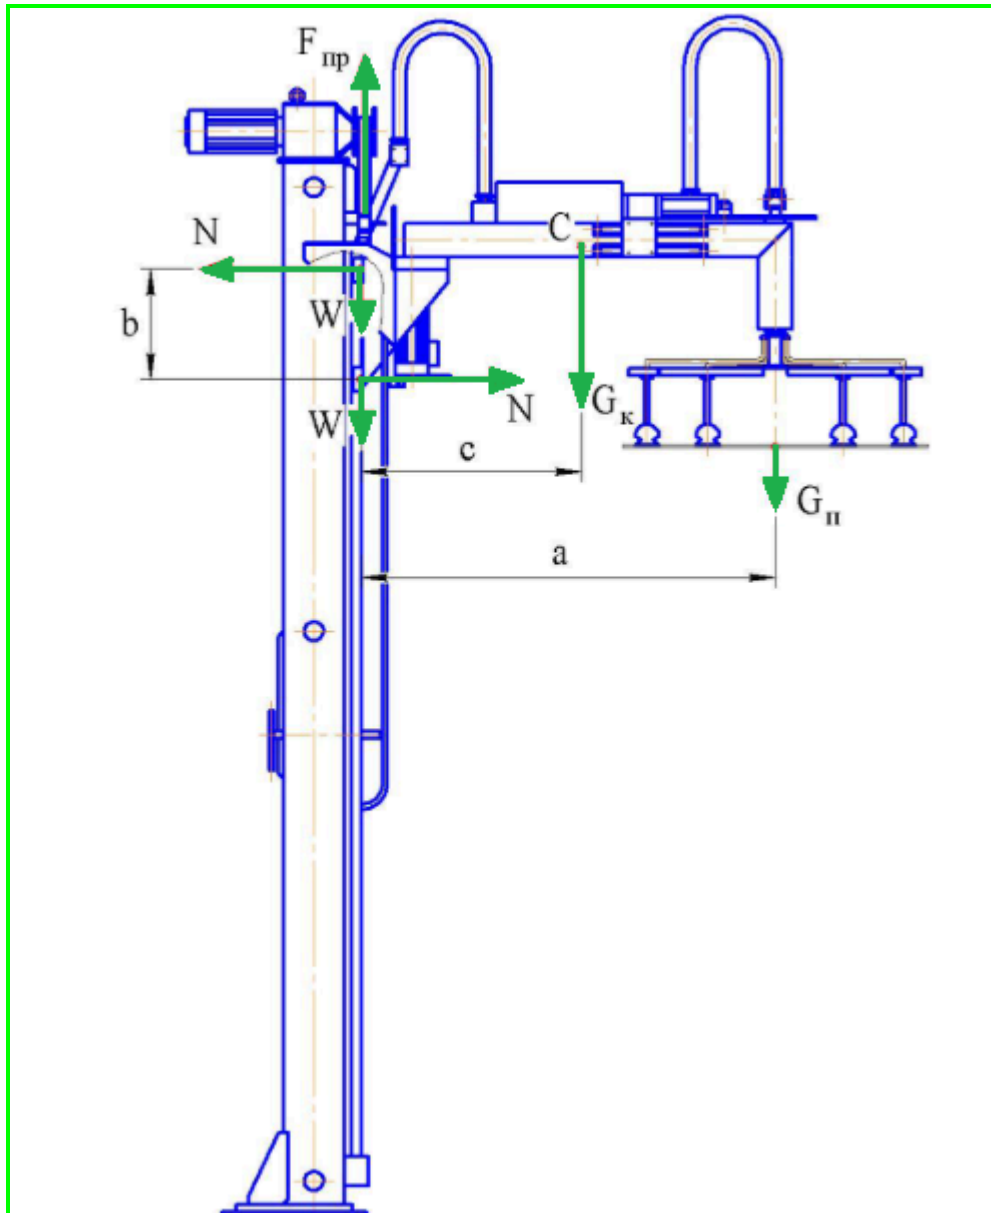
Схема навантаження на каретку вертикального переміщення
